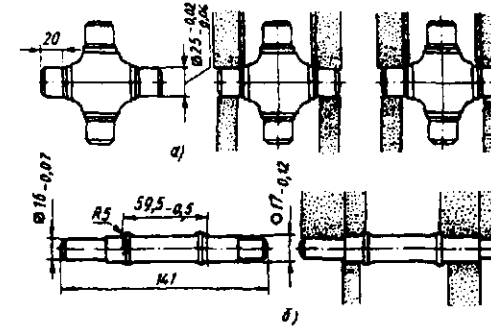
Схемы многокруговых наладок для обработки разобнесенных поверхностей: а – для обработки крестовины; б – для обработки ступенчатого валика
